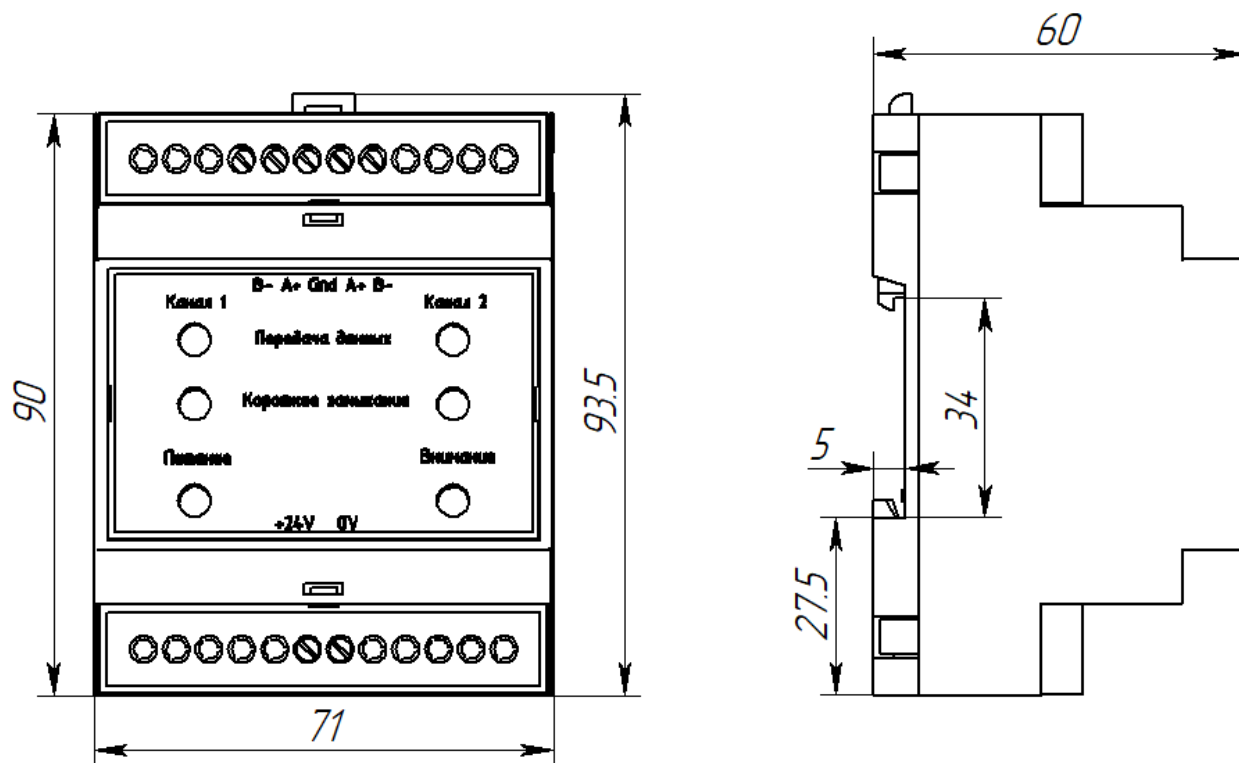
Внешний вид, габаритные и установочные размеры
